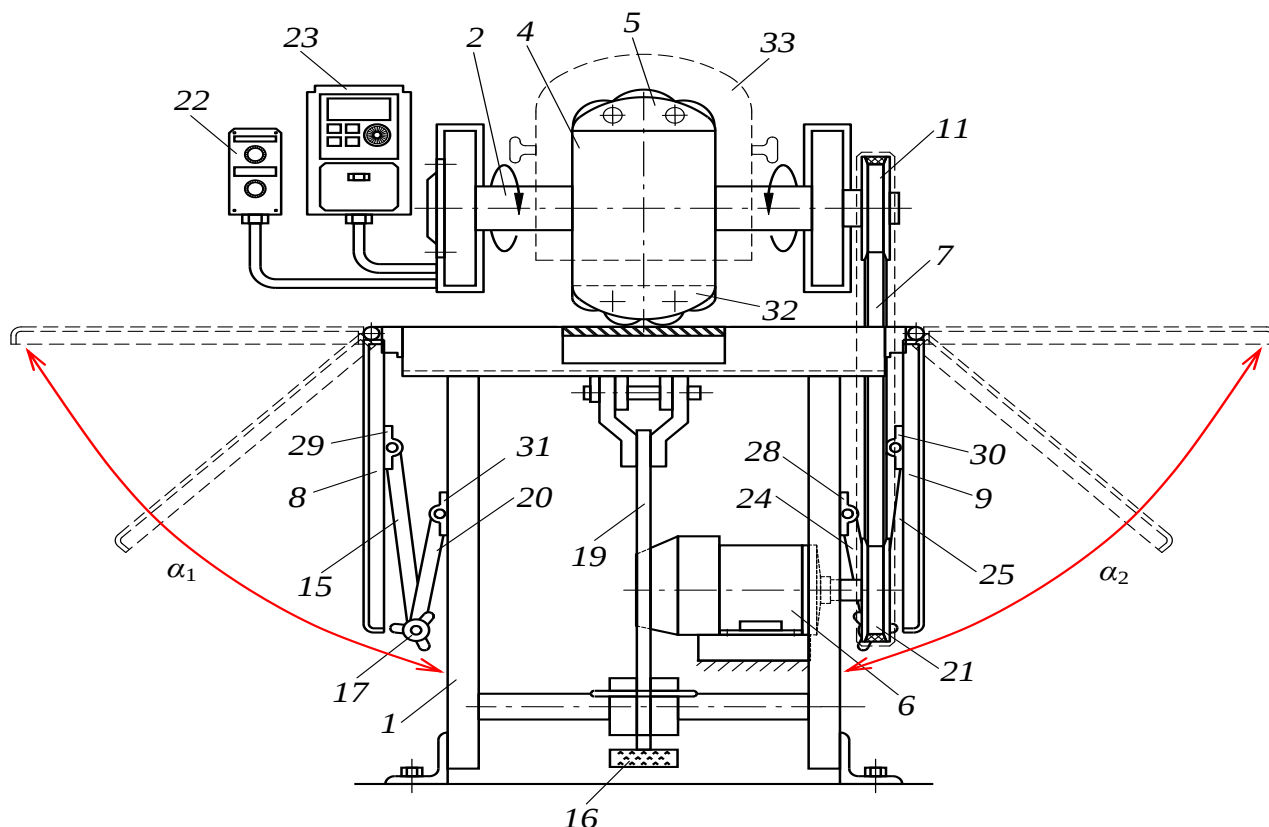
Схема разбивочной машины с боковыми подпорками
